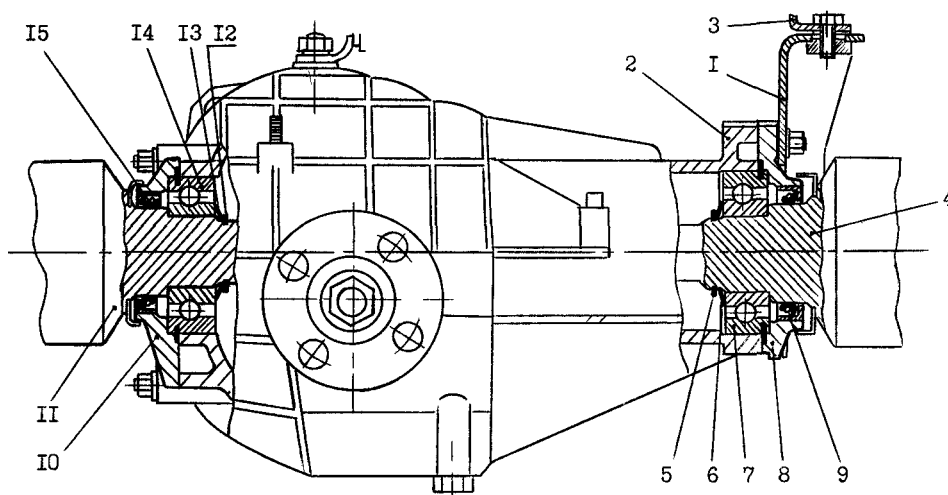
Встановлення внутрішніх шарнірів приводів :1-правий кронштейн підвіски переднього моста; 2-картер редуктора, 3-кронштейн підвіски двигуна; 4-вал внутрішнього шарніра правого приводу, 5-стопорне кільце; 6-шайба; 7-підшипник; 8-кришка підшипника; 9-сальник; 10-кришка підшипника; 11-вал внутрішнього шарніра лівого приводу, 12-стопорне кільце, 13-шайба; 14-підшипник; 15-сальник.
